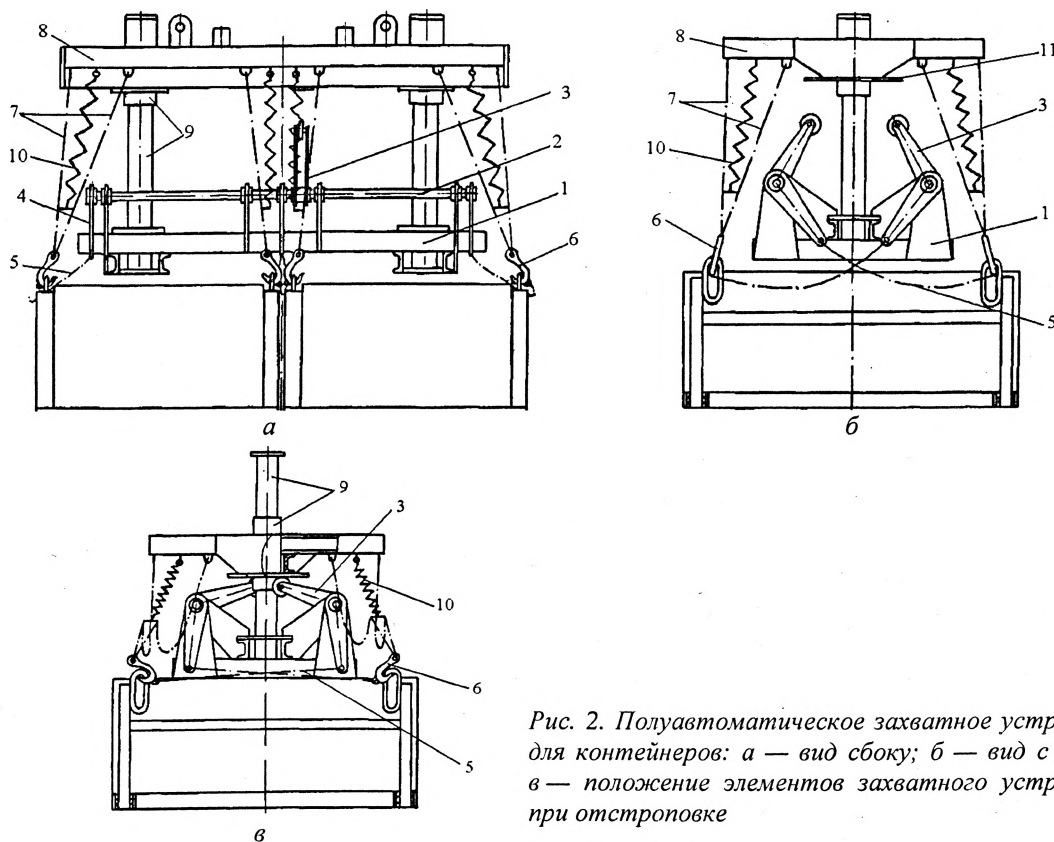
Полуавтоматическое захватное устройство для контейнеров: а — вид сбоку; б — вид с торца; в — положение элементов захватного устройства при отстроповке
